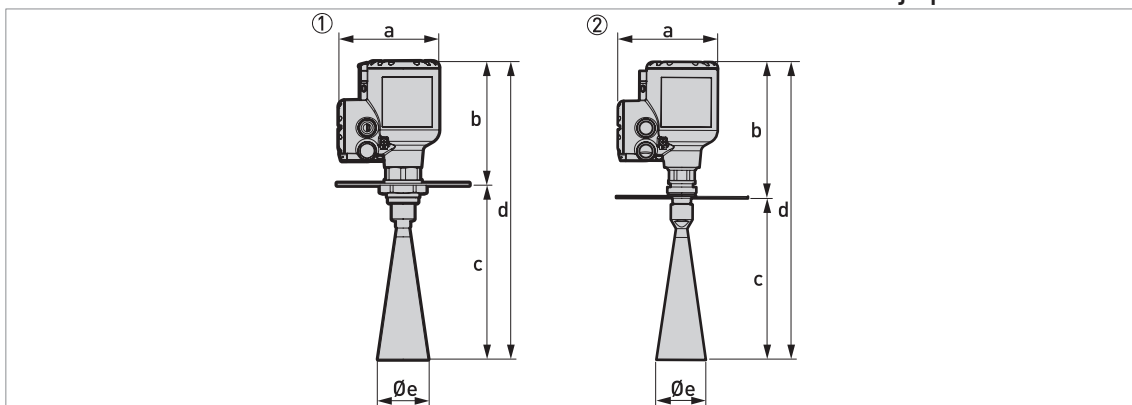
Antenas cónicas metálicas con conexiones con brida de baja presión
